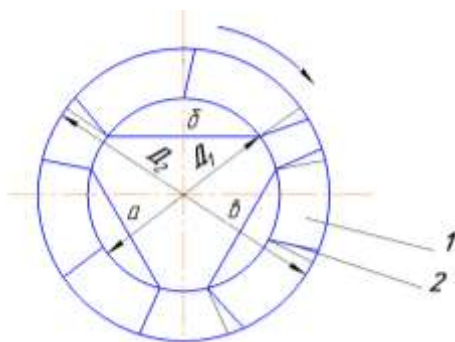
Ротор с прямолинейными лопатками: 1 – ротор; 2 – лопатка; а – радиальнооканчивающиеся; б – отогнутые вперед; в – отогнутые назад; D_1 и D_2 – внутренний и наружный диаметры ротора
